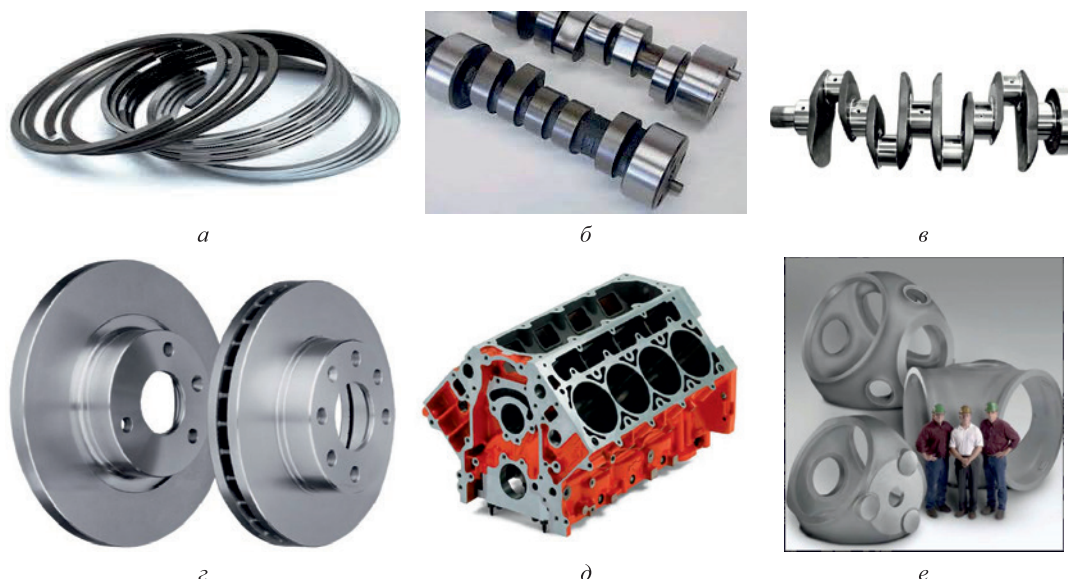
Примеры типовых машиностроительных деталей из чугуна: поршневые кольца (а); распределительные валы (б); коленчатый вал (в); тормозные диски (г); корпус блока цилиндров (д); корпуса современной ветряной электростанции (е)
